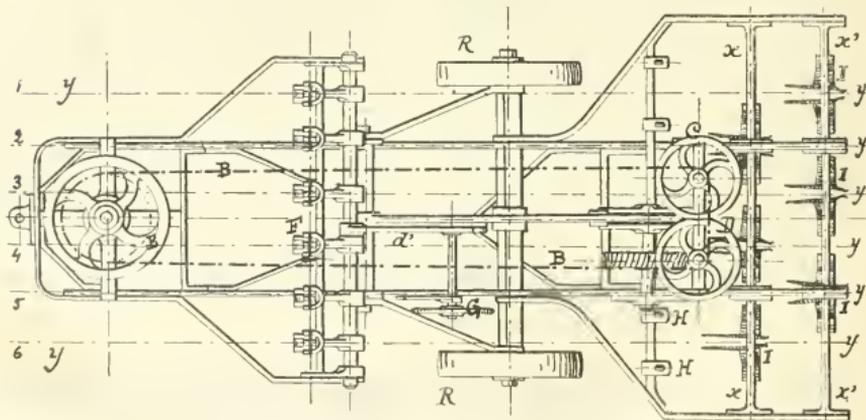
Plan de l'arracheur de betteraves à grand travail (A. Bajac.)
